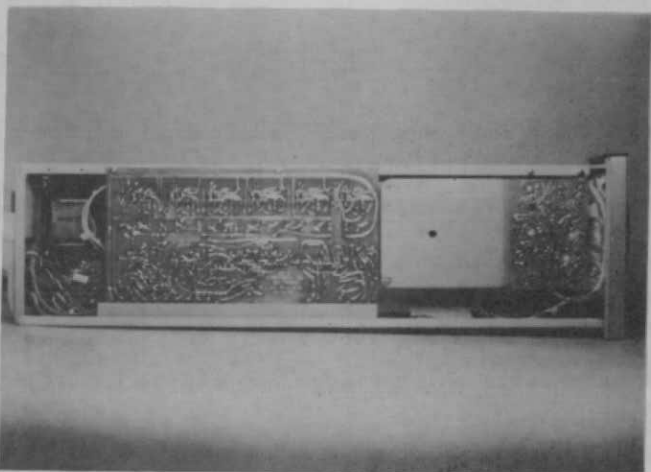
Placa de circuito impresso instalada no HIC-8903.
